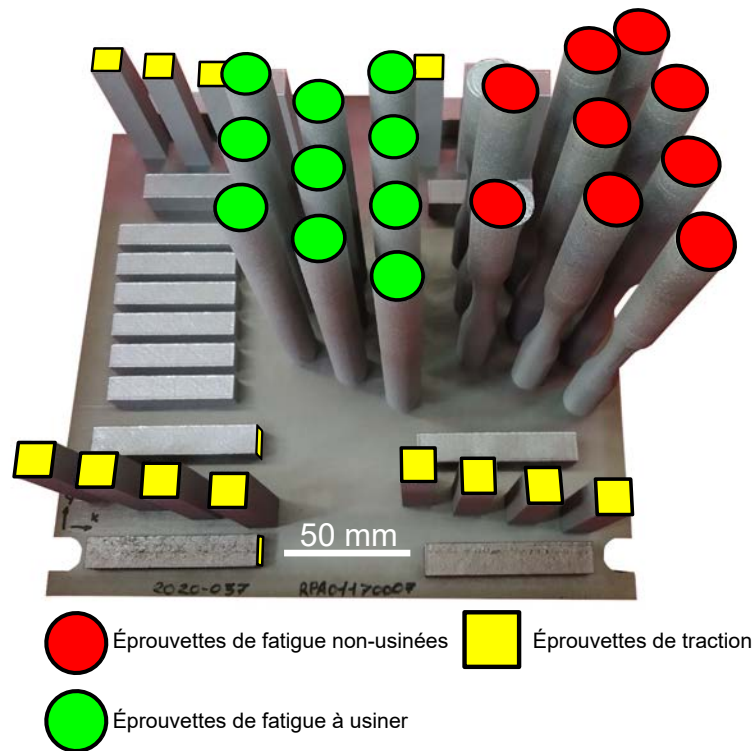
Plateau de fabrication présentant des éprouvettes de fatigue et de traction en PM420. Toutes les éprouvettes de fatigue ont été imprimées verticalement. Quant aux éprouvettes de traction, ici destinées à Aubert & Duval, celles-ci ont été imprimées horizontalement et verticalement.
